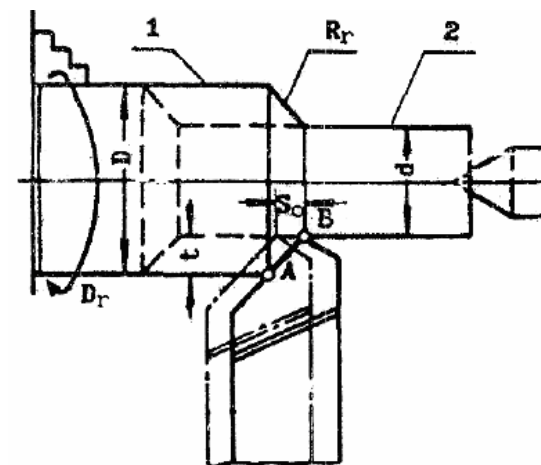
Схема наружного точения (обтачивания); 1 – обрабатываемая поверхность; 2 – обработанная поверхность; R_r – поверхность резания; D – диаметр обрабатываемой поверхности; d – диаметр обработанной поверхности; D_r – главное движение резания; D_s – движение подачи; t – глубина резания; S_v – подача на оборот; А, Б – точки обрабатываемой и обработанной поверхностей, находящиеся на поверхности резания.
